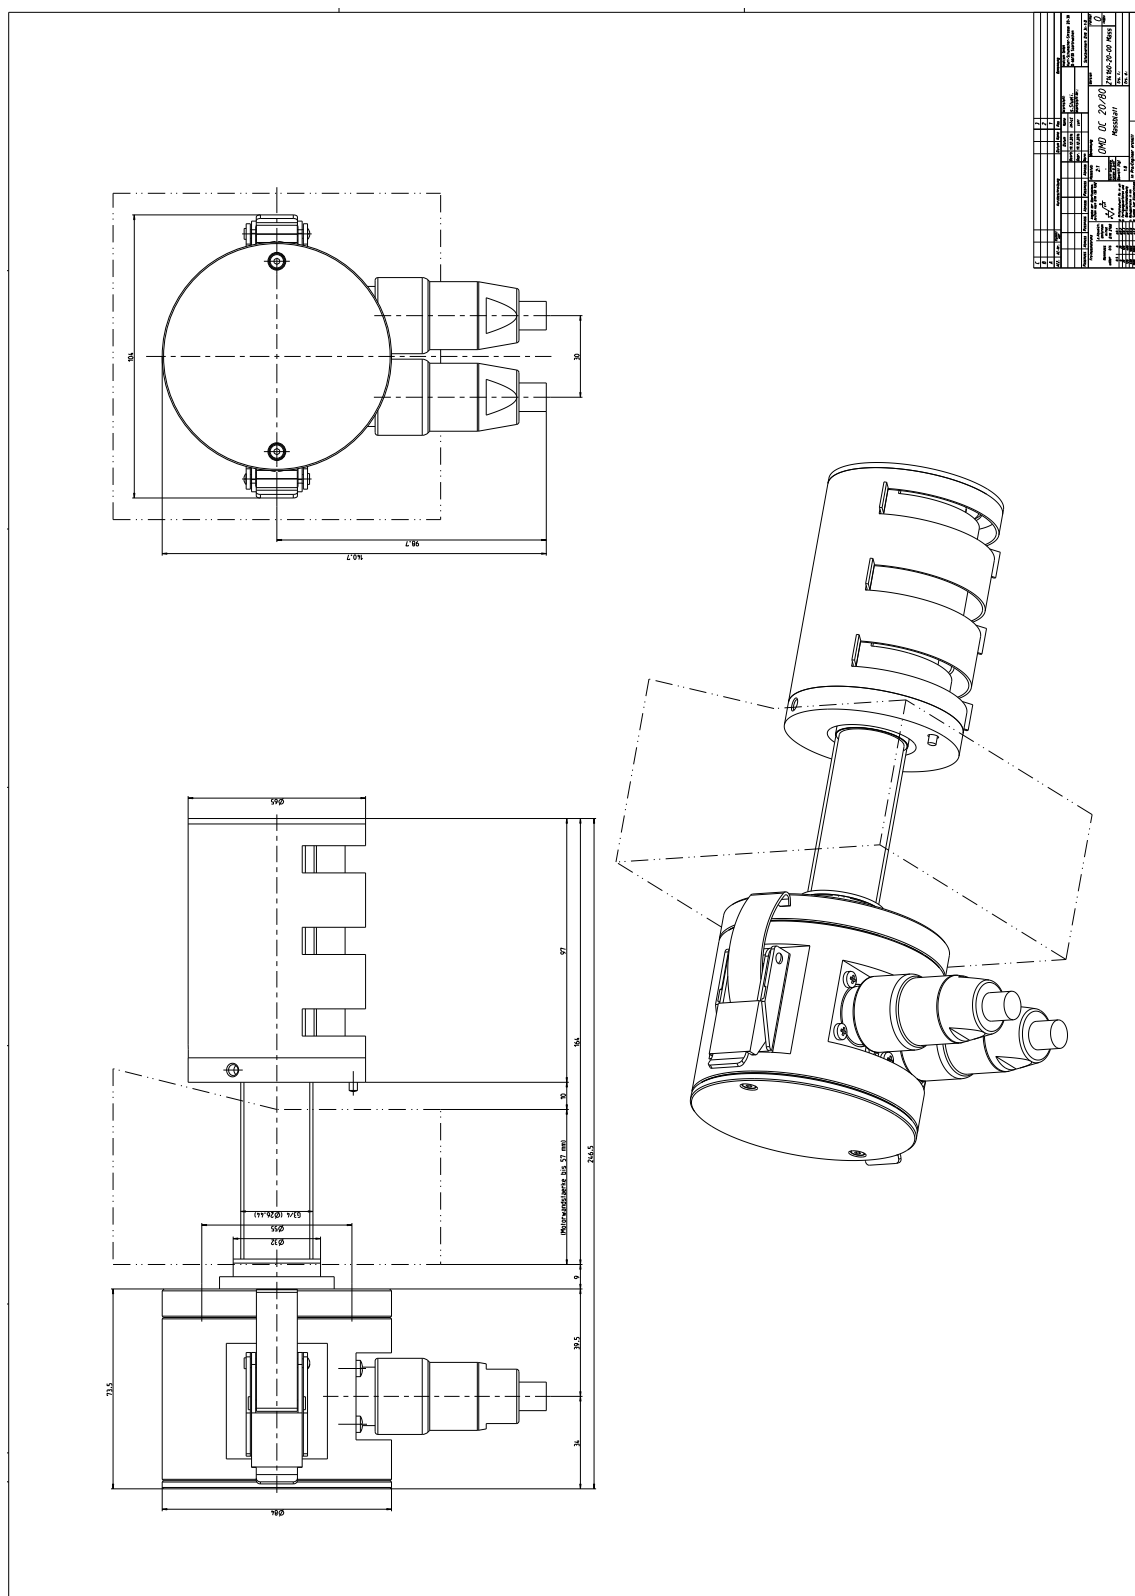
Dimensiones del sensor SiCOMS® de tipo SiSe/OC20-80
